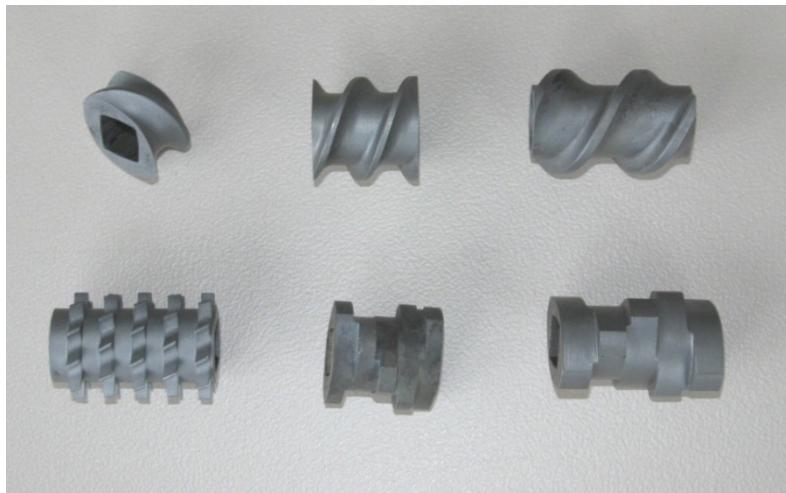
Elementos seccionales que componen un tornillo de un sistema de extrusión de doble tornillo. Fuente: Brabender® GmbH & Co.
